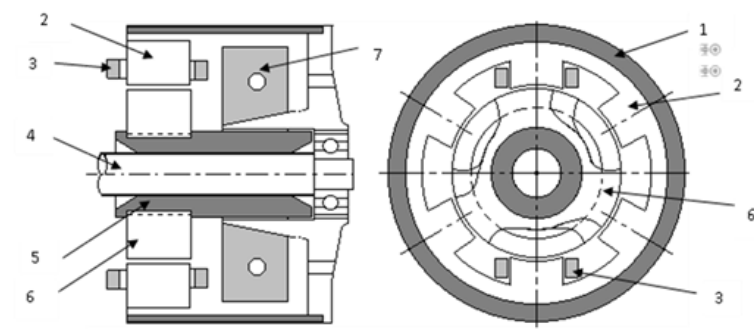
Однопакетный индукторный генератор униполярного типа
